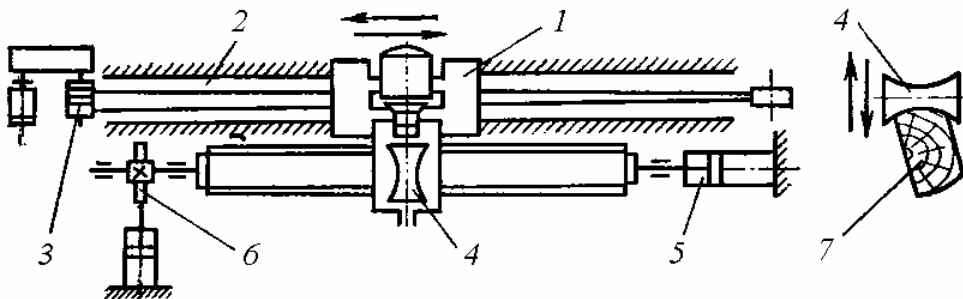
Схема шпалооправочного станка ЛО-44Б: 1 – каретка; 2, 3 – направляющие и привод каретки; 4 – барабанная ножевая головка; 5, 6 – механизм зажима и поворота шпалы; 7 – шпала
